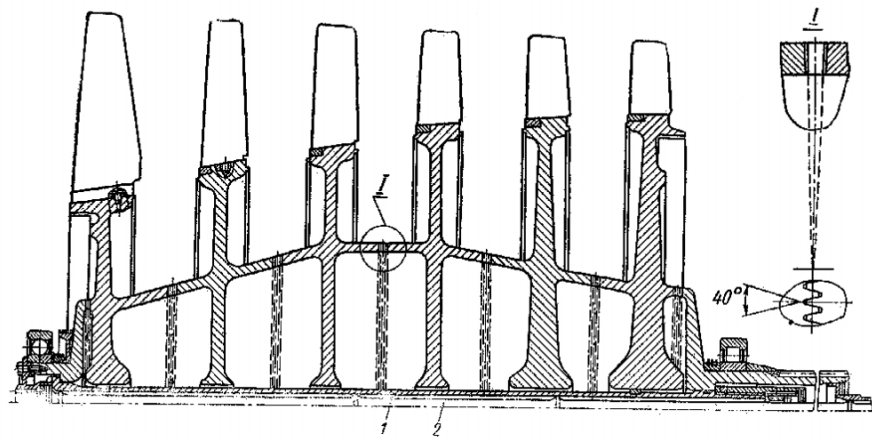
Ротор компрессора с соединением секций с помощью торцевых треугольных шлицев и стяжного болта:
